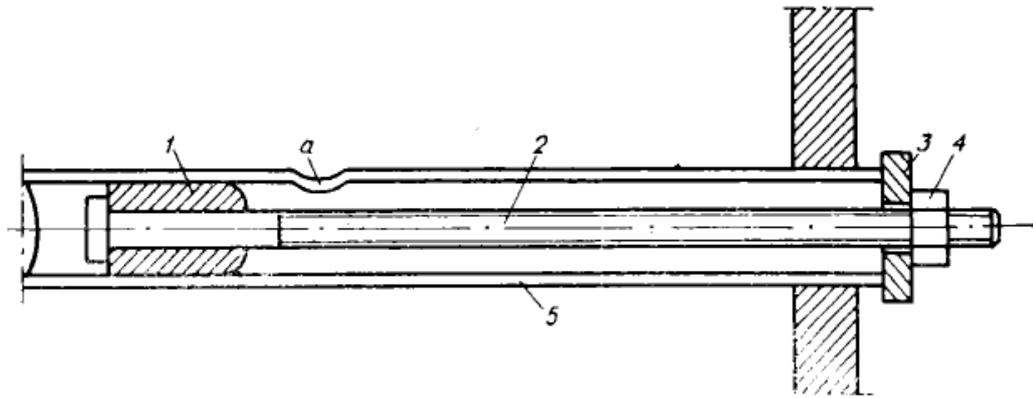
Приспособление для правки вмятин в трубах: 1 – оправка; 2 – штанга с резьбой; 3 – шайба; 4 – гайка; 5 – труба; а – вмятина.
